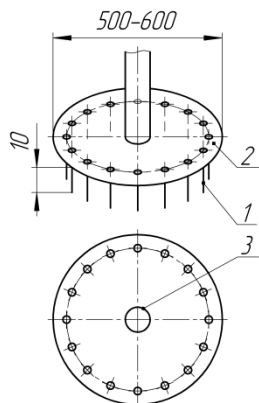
Схема насадки для обработки кустовых зон: 1 – нож; 2 – диск; 3 – ротор
